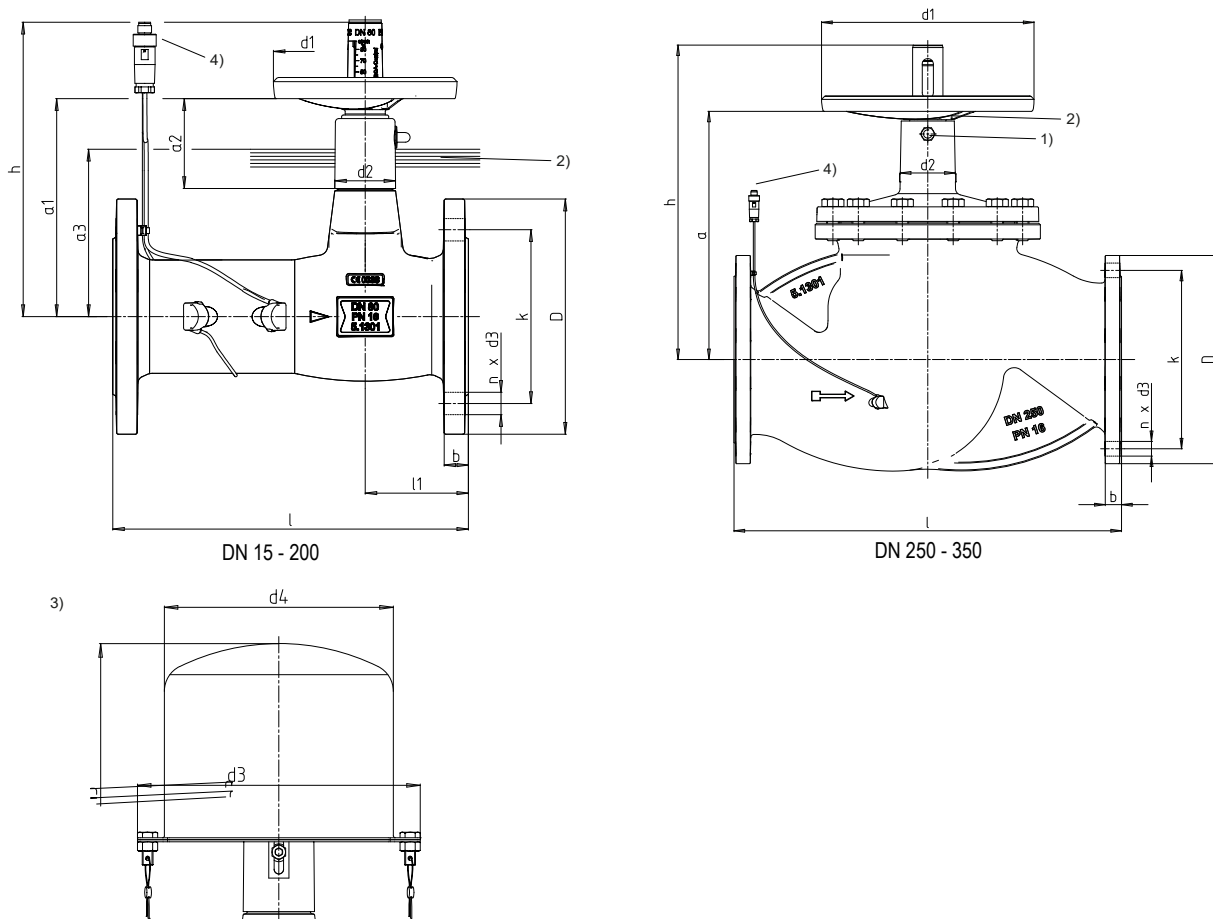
Dimensioni; BOA-CL DN 15 - 200, BOA-H DN 250 - 350
